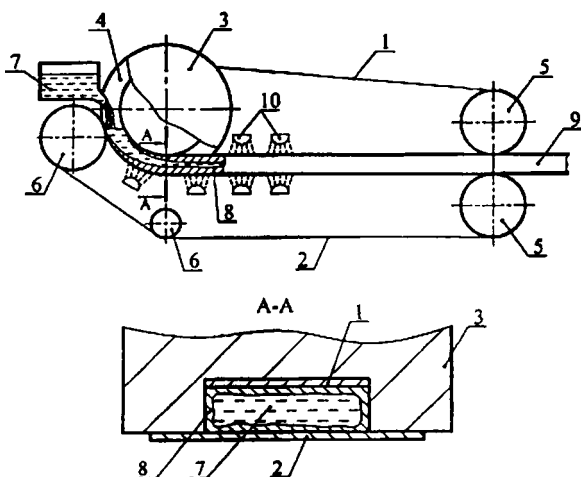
Схема установки непрерывного литья полос: 1, 2 – лента; 3 – барабан; 4 – проточка; 5 – ролик приводной; 6 – ролик натяжной; 7 – расплав; 8 – начальная корка; 9 – отливка; 10 – водяное охлаждение
